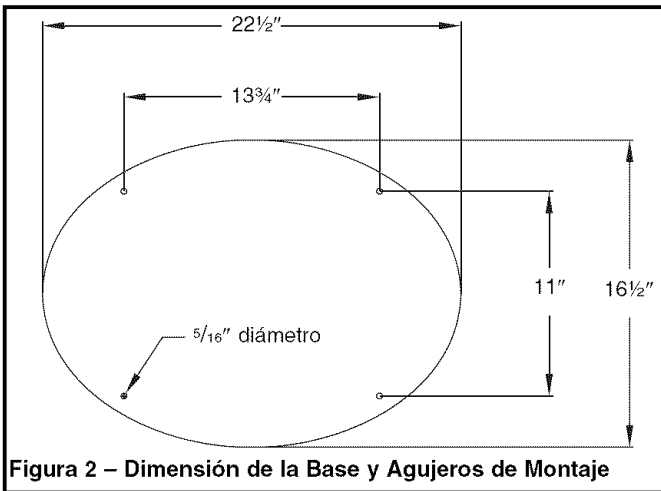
Dimensión de la Base y Agujeros de Montaje
